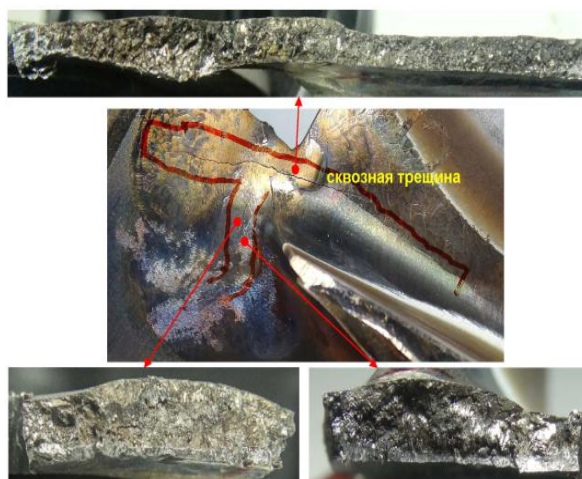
Злами за розкритими тріщинами на передньому корпусі двигуна РД-33.
